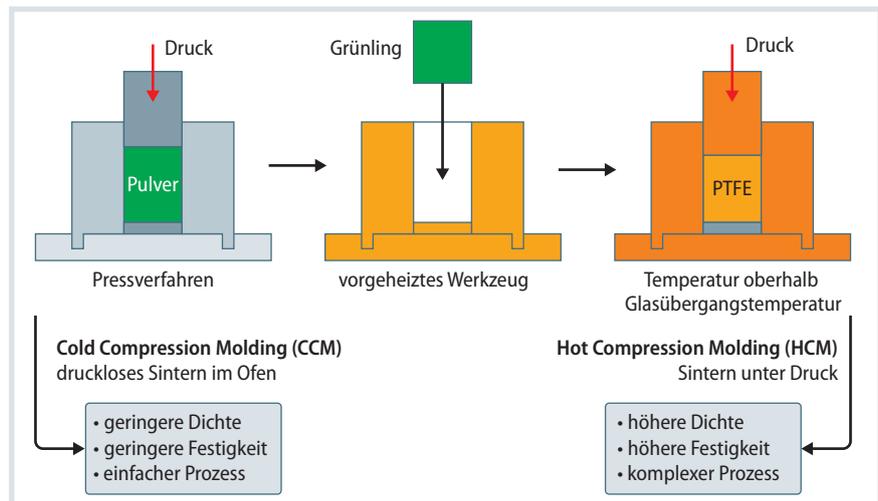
PTFE lässt sich im Cold- und im Hot-Compression-Molding-Verfahren verarbeiten
